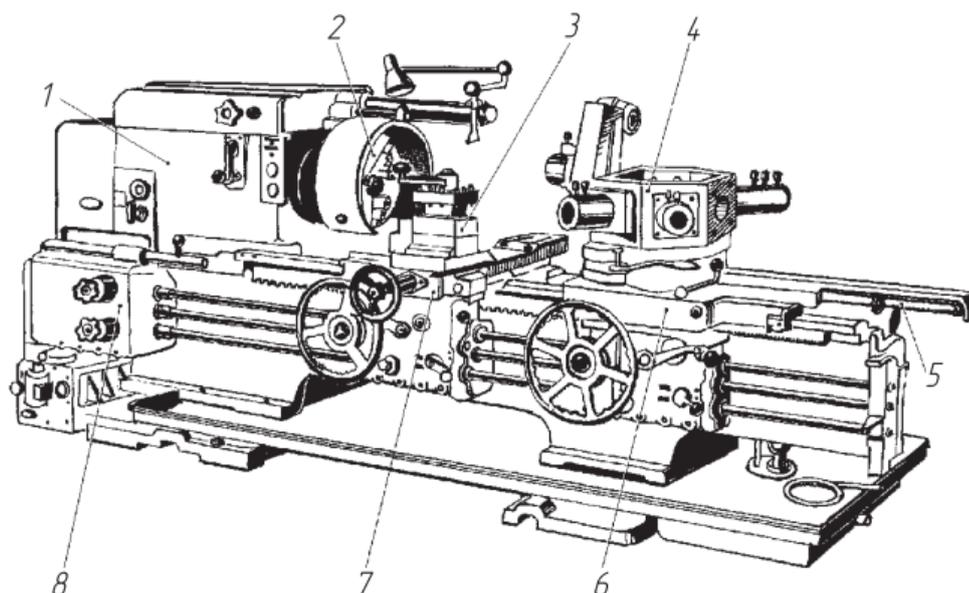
Токарно-револьверный станок модели 1ПЗ71: 1 – передняя бабка с коробкой скоростей; 2 – шпиндель с патроном; 3 – резцедержатель поперечного суппорта; 4 – револьверная головка; 5 – барабан продольных упоров; 6 – револьверный суппорт; 7 – поперечный суппорт; 8 – коробка подач.
